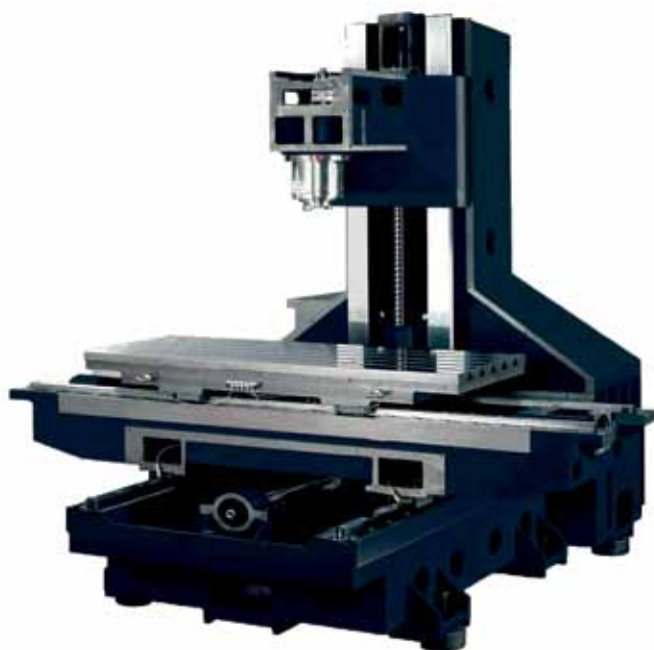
Конструкция станины обрабатывающего центра KBC B4
